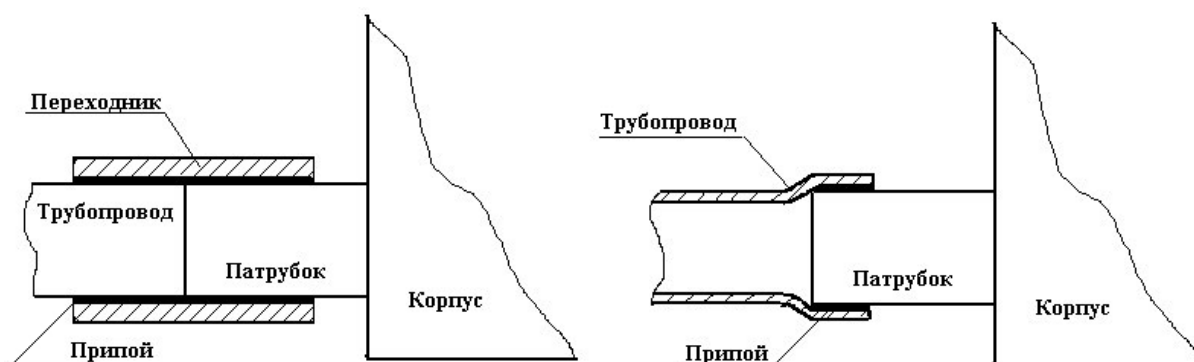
Способы соединения патрубка агрегата компрессорного с трубопроводом
